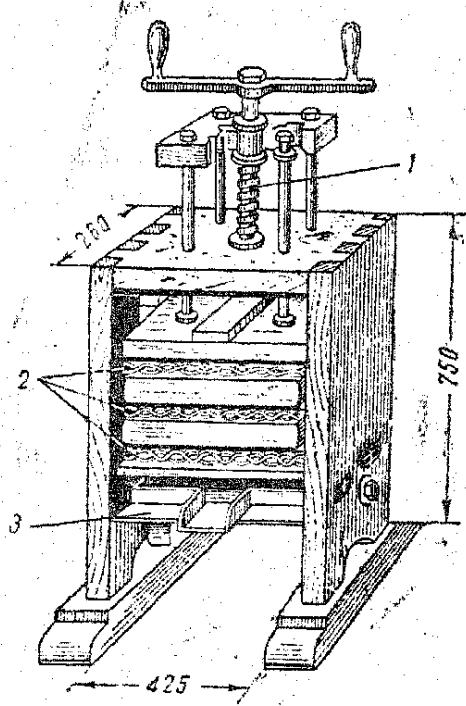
Деревянный ручной пресс: 1 — винт с неоднородной резьбой в три нитки на 1 дюйм; 2 — пластины из яловых прутьев; 3 — поддон из жести
